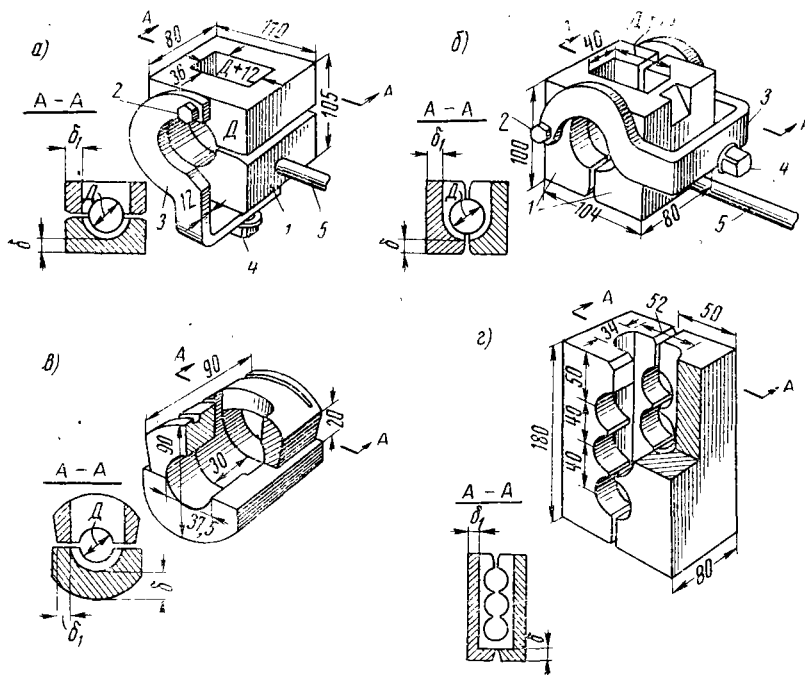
Конструкции инвентарных составных медных форм с канавками для сварки стыковых соединений горизонтальных стержней:
